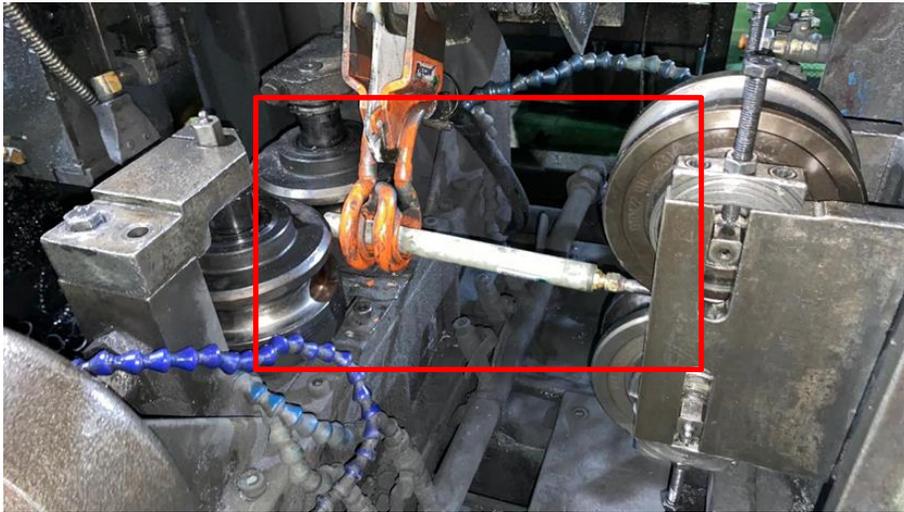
3 Impeder diámetro 18mm. Fuente CMA Automotive
